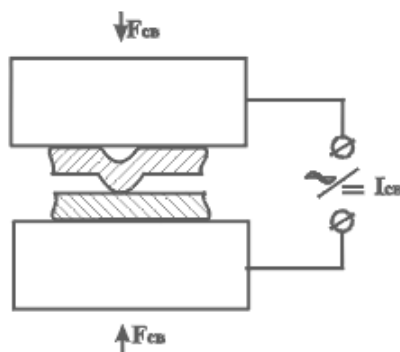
Схема рельефной контактной сварки.
